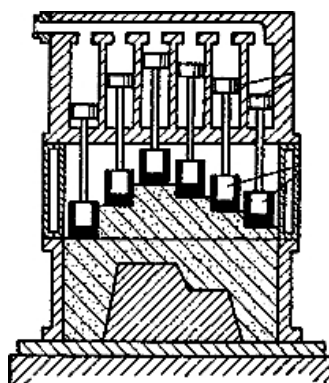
Технологічний процес верхнього пресування суміші багатоплунжерних головою: 1 – корпус головки; 2 – поршні; 3 – пресуючі плунжери
